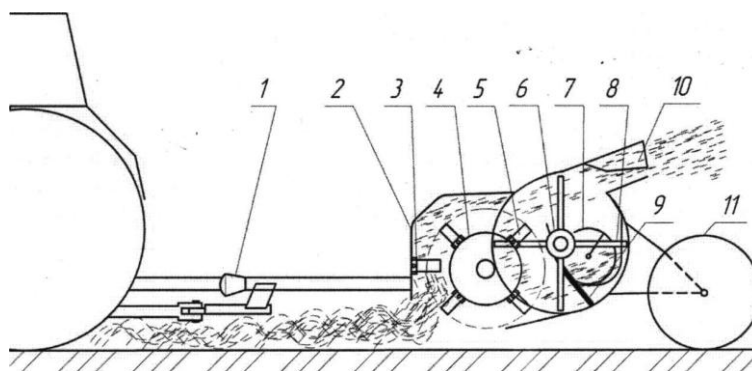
Технологическая схема 2 прицепного измельчителя-разбрасывателя соломы с двухстадийным измельчением: 1 - карданный вал; 2 - корпус измельчителя; 3 - противорезы; 4 - роторный подбирающий аппарат (измельчающий барабан); 5 - нож измельчающего барабана; 6 - барабан доизмельчитель; 7 - шнек; 8 - нож; 9 - противорезущая пластина; 10 - распылитель; 11 – колесо
